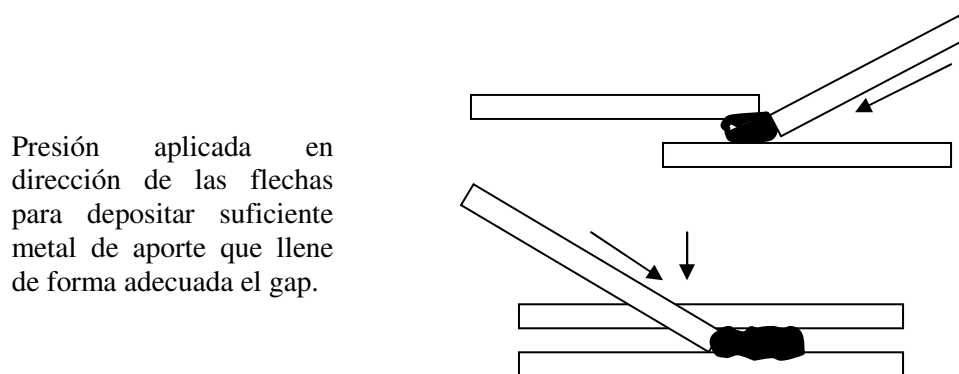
Técnica de alimentación para soldaduras de filete con abertura mayor a 1/8" [11].
